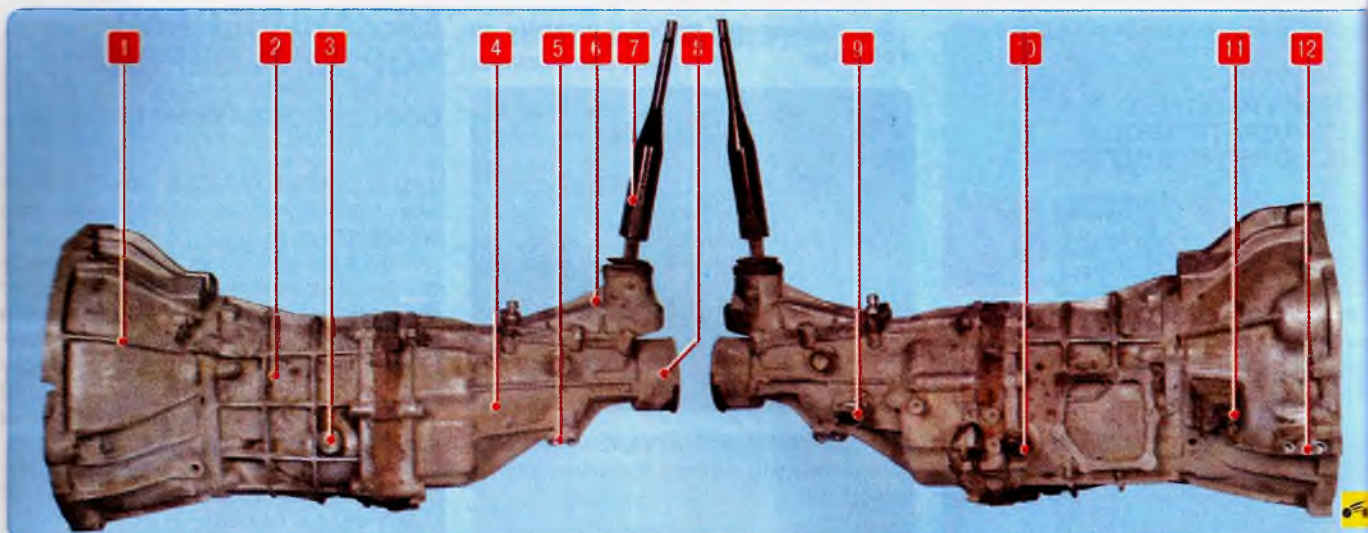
Механическая коробка передач: 1 – картер сцепления; 2 – картер коробки передач; 3 – пробка контрольного (наливного) отверстия; 4 – задняя крышка коробки передач; 5 – отверстия болтов крепления задней опоры подвески силового агрегата; 6 – крышка механизма переключения передач; 7 – рычаг переключения передач; 8 – выходной вал коробки передач; 9 – датчик скорости; 10 – выключатель фонарей света заднего хода; 11 – вилка выключения сцепления; 12 – отверстия болтов крепления рабочего вала сцепления
